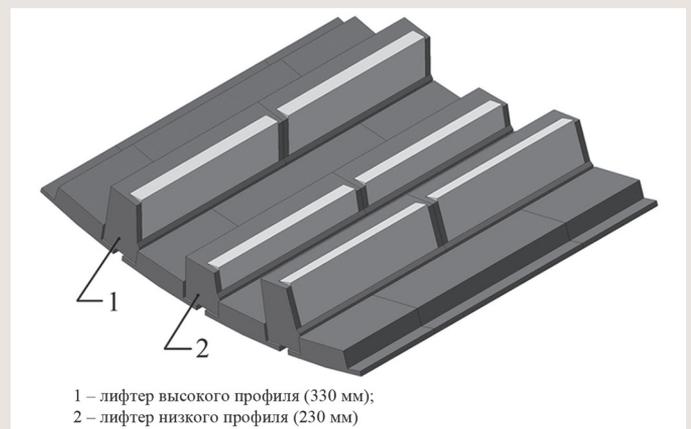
Общий вид резиновой футеровки барабана мельницы.
